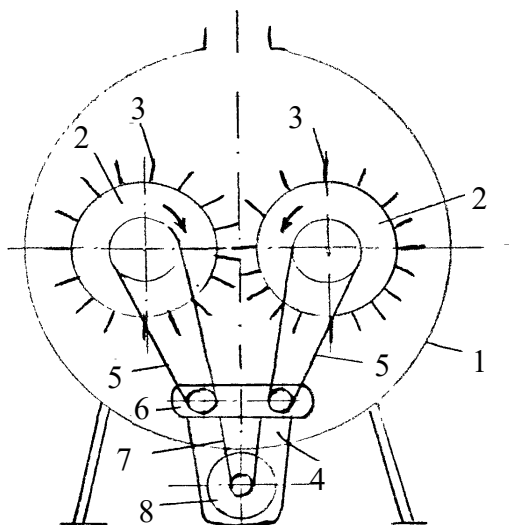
Схема бильно-душової машини: 1 – корпус; 2 – барабан; 3 – били; 4 – привід; 5, 7 – клинопасова передача; 6 – редуктор; 8 – електродвигун
